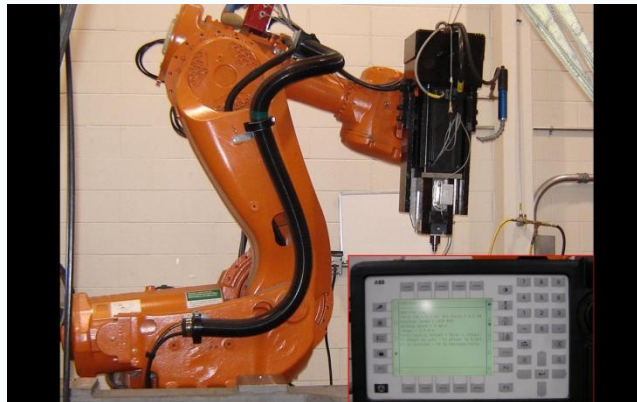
Robot diseñado para la Soldadura de Fricción - Agitación
